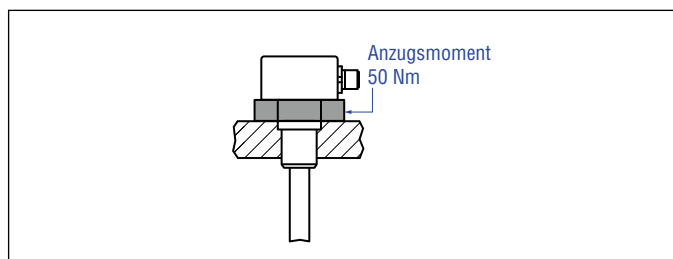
Einbaubeispiel für Gewindeflansch »M« & »T«
